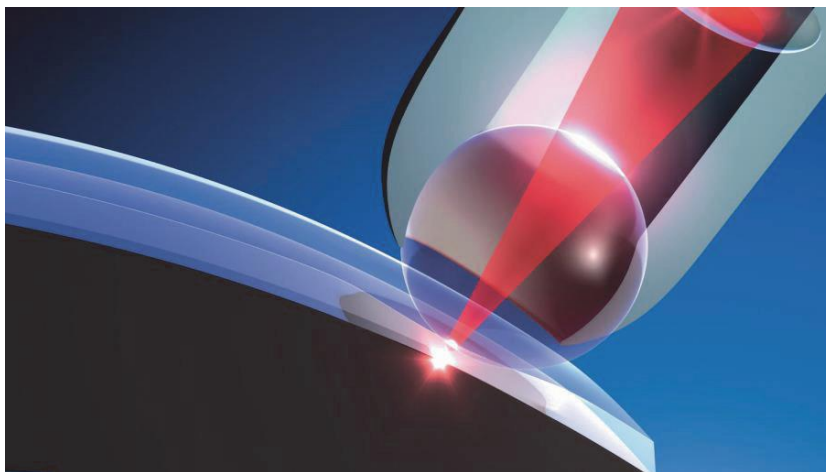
Globo-Welding* Laserschweißverfahren der *Fa. Leister*, Darstellung aus (*Leister Technologies AG o.J.a*)
